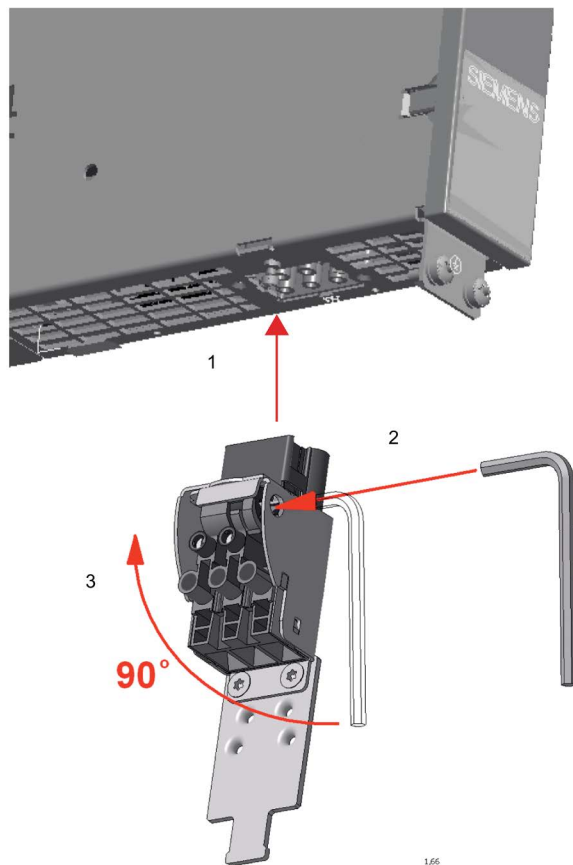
Montaje tomando como ejemplo un conector atornillable
